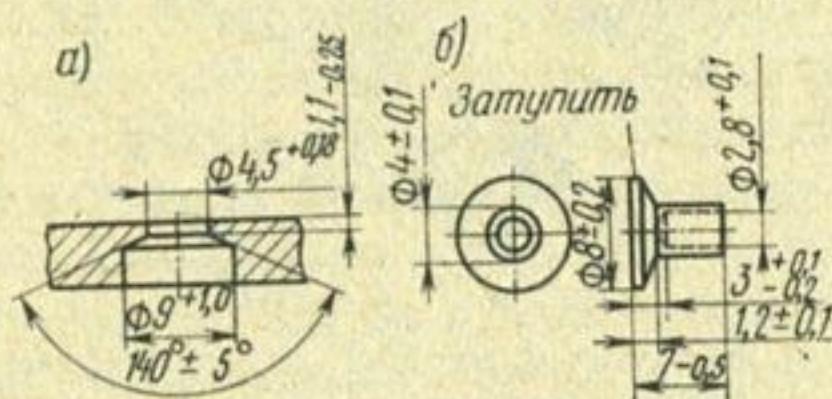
Размеры заклепки и отверстия для нее во фрикционной накладке тормозной колодки:
